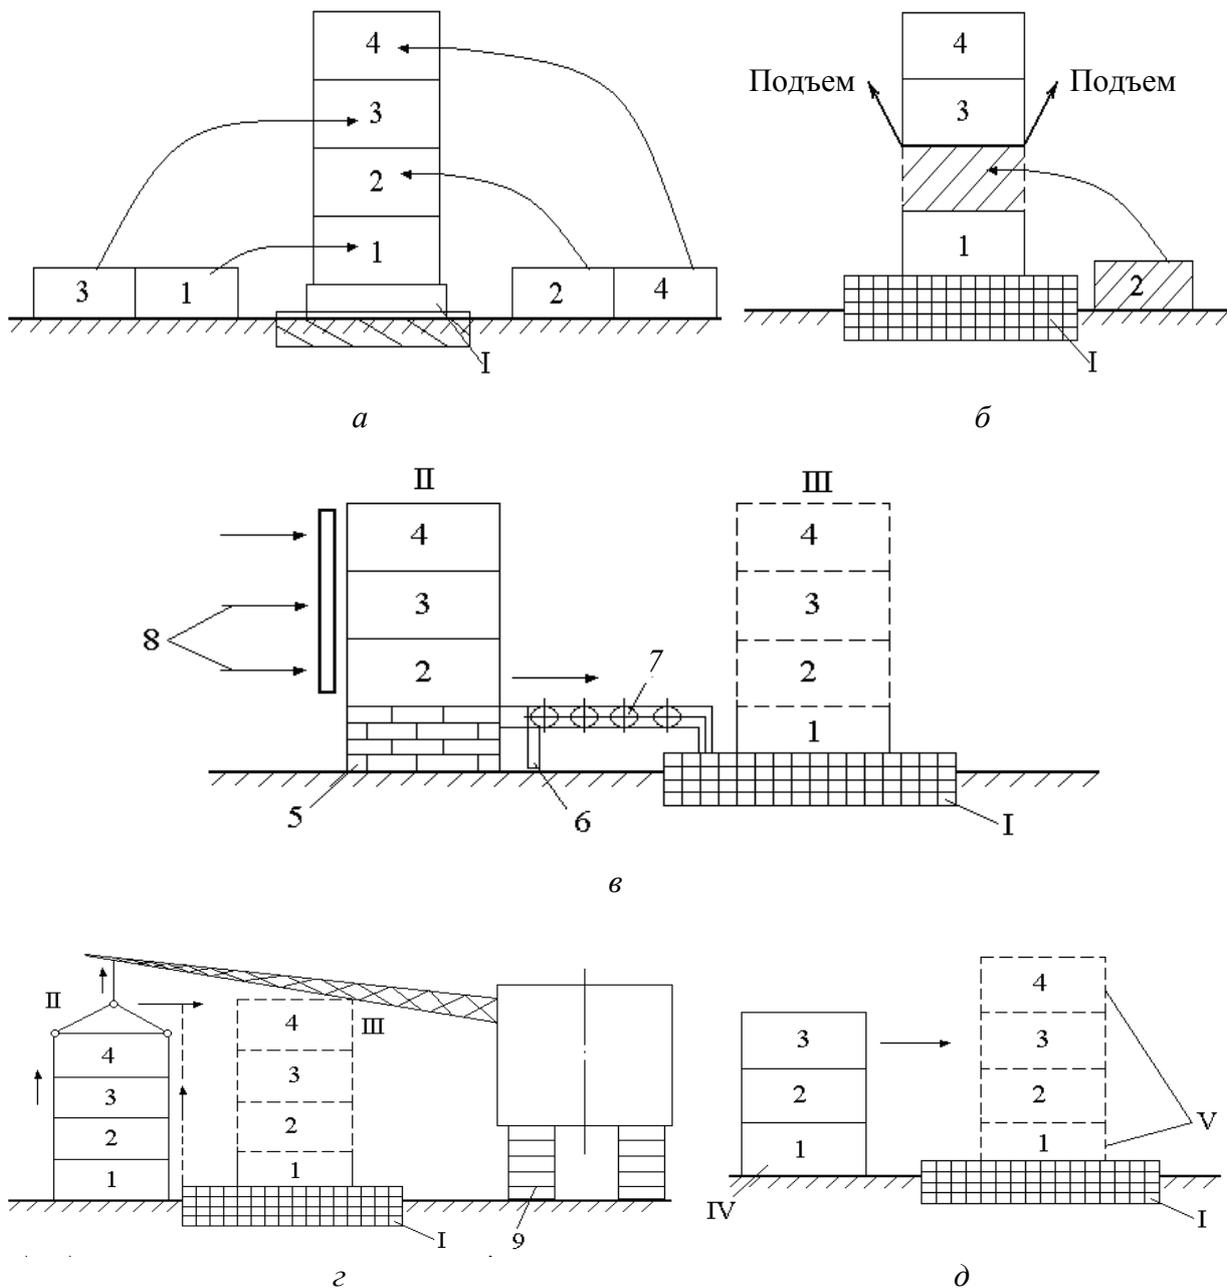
Способы монтажа и сборки узлов: *а* – последовательный монтаж: I – фундамент; 1 – база; 2–4 – узлы; *б* – ступенчатый монтаж: I – фундамент; 1 – база; 2 – узел, подводимый под верхние узлы; 3, 4 – верхние узлы; *в* – монтаж надвигкой узла: I – фундамент; 1 – база; 2–4 – верхние узлы; 5 – стенд; 6 – настил; 7 – катки; 8 – устройство для передвижки; 9 – кран; II – монтаж узлов на стенде; III – проложение узлов на фундаменте; *г* – сборка машины на стенде и перенос на фундамент краном: I – фундамент; 2–4 – узлы; 9 – кран; II – монтаж узлов на стенде; III – положение узлов на фундаменте; *д* – сборка основных узлов с одновременным укрупнением: I – фундамент; IV – сборка и укрупнение узлов на стенде; V – окончательный монтаж на фундаменте
